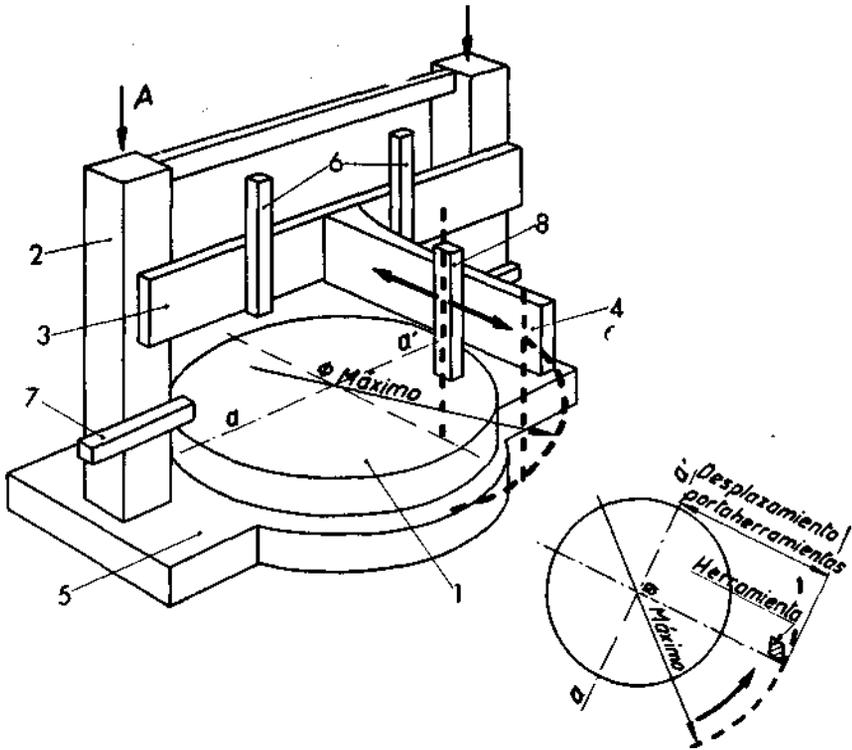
Montaje de una consola para ampliar el diámetro máximo a tornearse: 1, plato portapieza; 2, montantes; 3, traviesa; 4, consola; 5, bancobastidor; 6, carros sobre traviesa; 7, carro sobre montante; 8, carro sobre consola. — a-a: eje de desplazamiento de las herramientas de los carros sobre traviesa.
